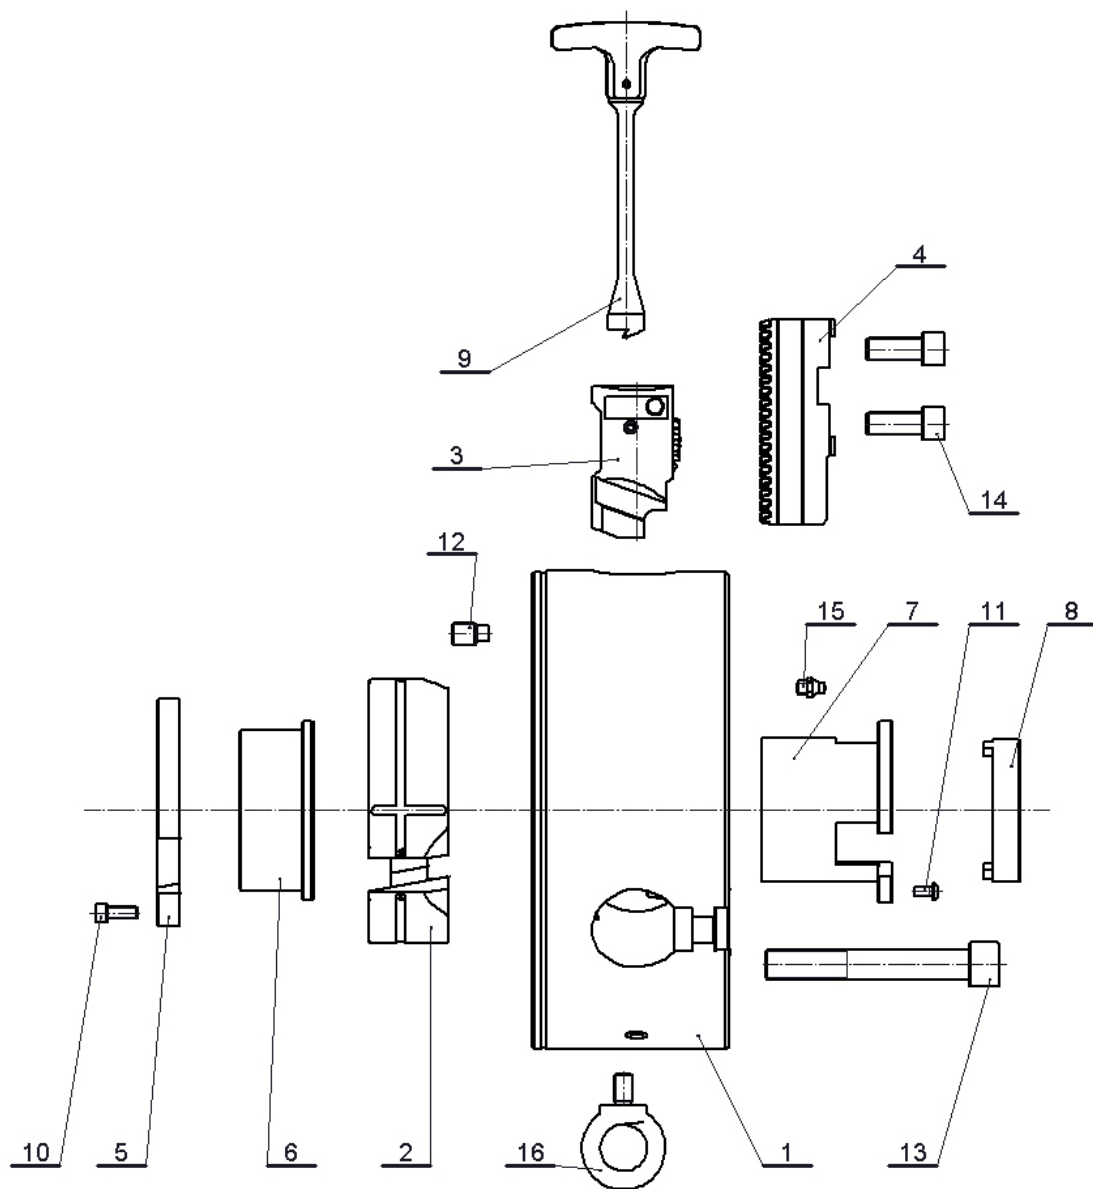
Bestandteile des mechanischen Spannfeeders mit Backenschnellwechselsystem
